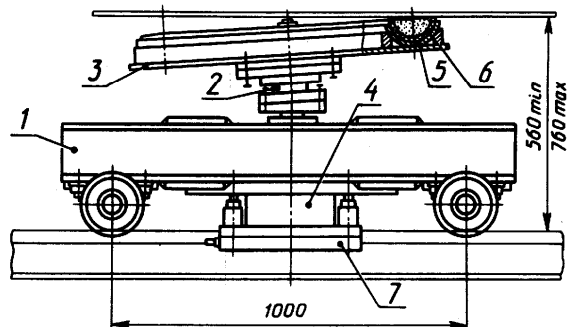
Резиновая подушка с эластичным лотком для сварки кольцевых швов
